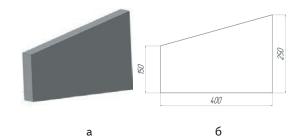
Схема диффузорного канала: а — 3D модель диффузорного канала; б — схема диффузорного канала
